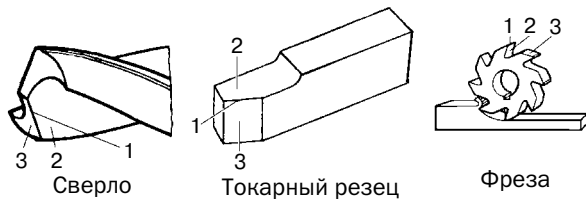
Режущие инструменты: 1 — режущая кромка, 2 — передняя поверхность, 3 — задняя поверхность
